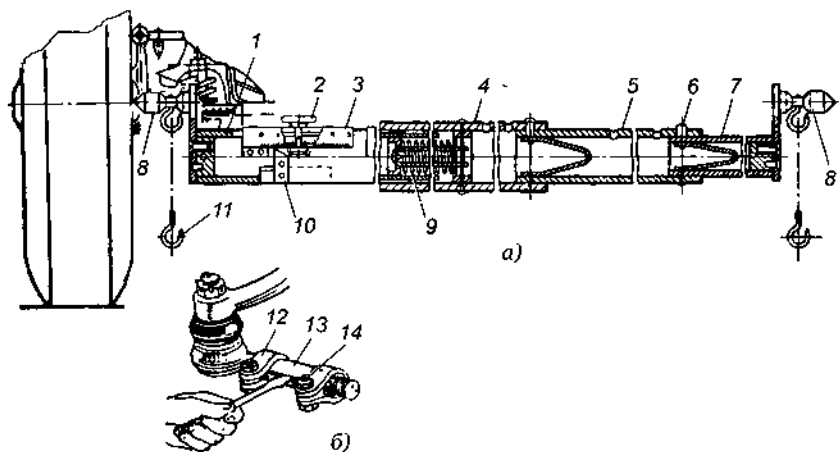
Линейка 2182 для измерения схождения колес: *a* — установка линейки на переднем мосту; *б* — регулировка длины поперечной тяги; 1 — подвижная труба; 2 — фиксирующий винт; 3 — шкала; 4 — неподвижная труба; 5 — промежуточная труба; 6 — фиксатор; 7 — удлинитель; 8 — наконечник; 9 — пружина; 10 — стрелка; 11 — цепочка; 12 — болт с гайкой; 13 — разрезная втулка; 14 — стяжной болт с гайкой
